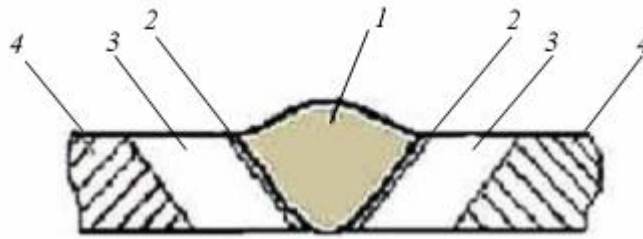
Строение стыкового сварного соединения:
